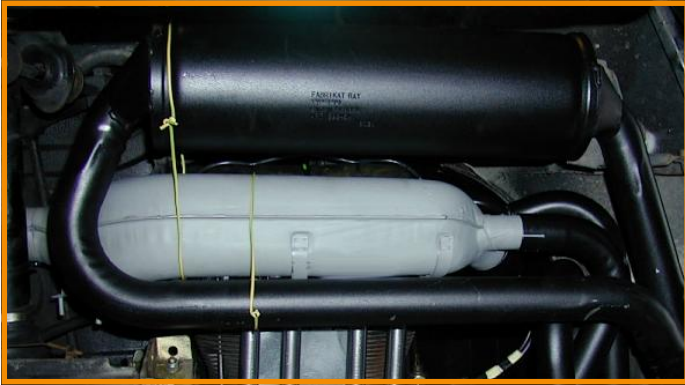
Ausrichten der Schalldämpfer zum Wärmetauscher
